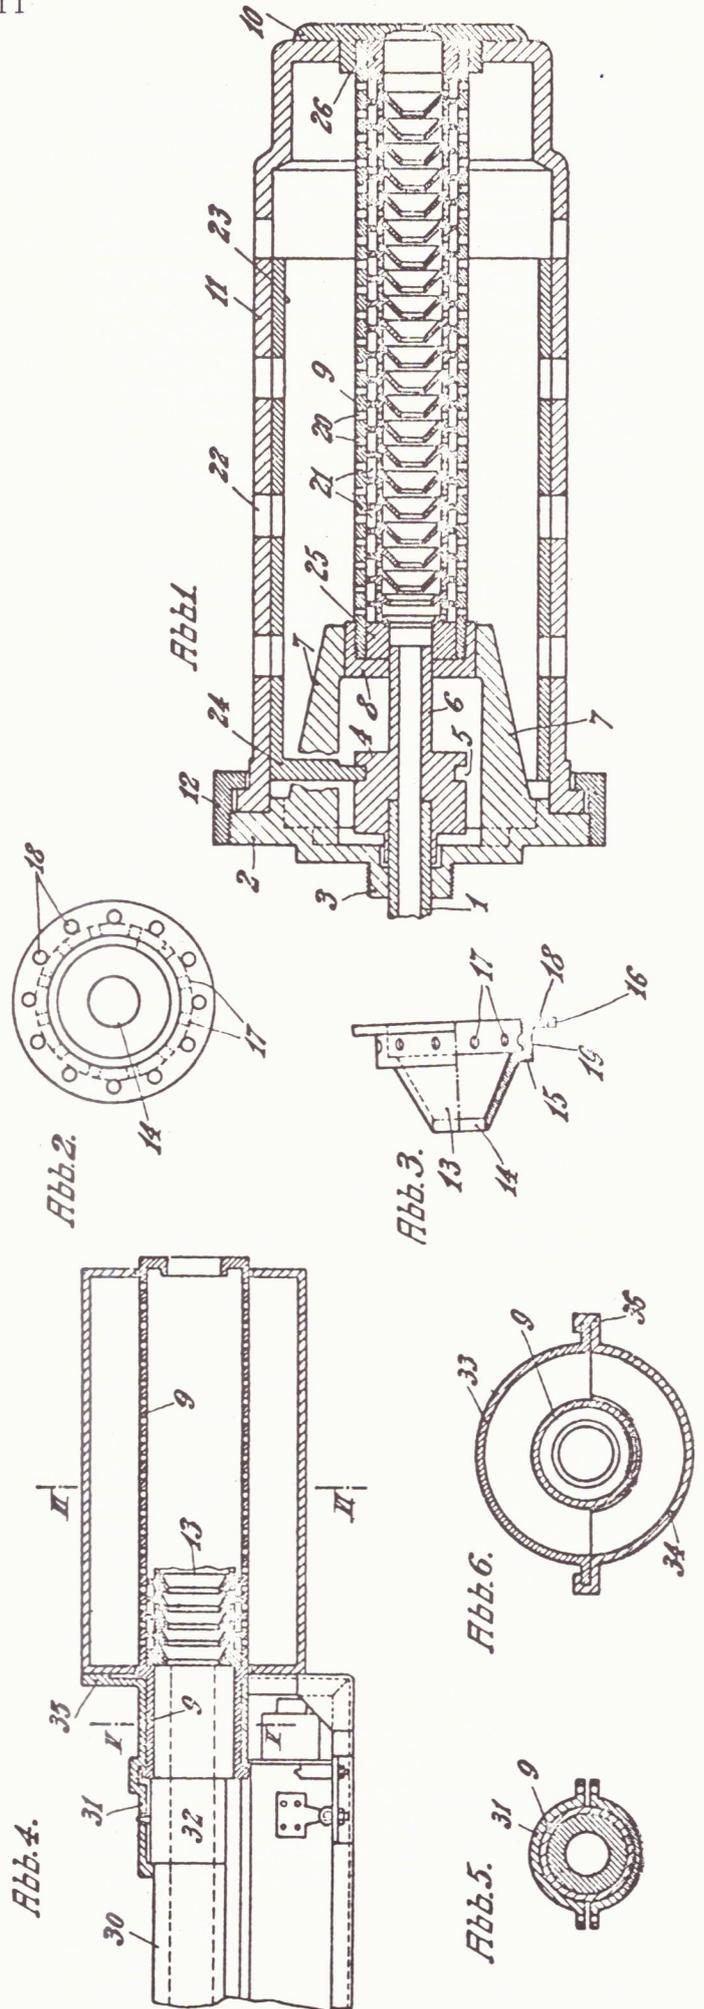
ist ein Längsschnitt durch die erste Ausführungsform;
